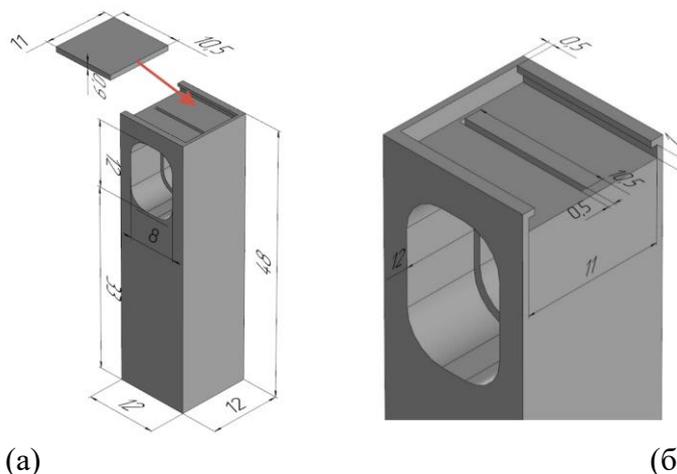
Кассета Б с линейными размерами: а – вид сбоку; б – вид сверху
